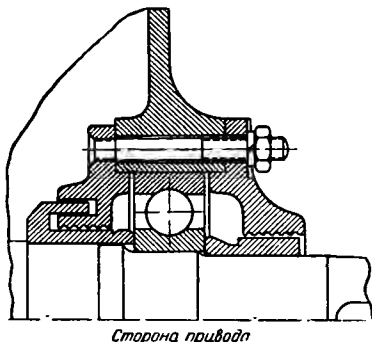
Подшипниковый узел с шарикоподшипником.
